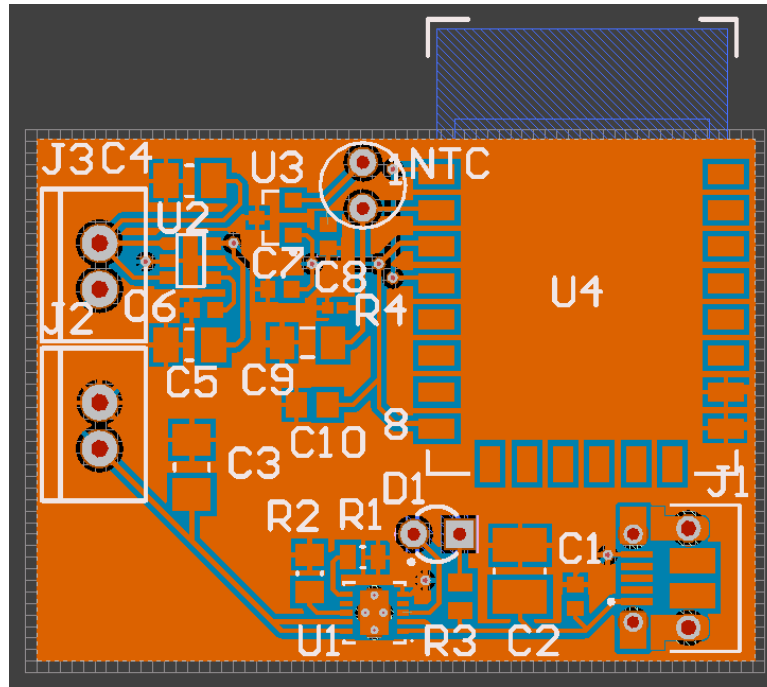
Cara superior de la PCB diseñada con componentes SMD
